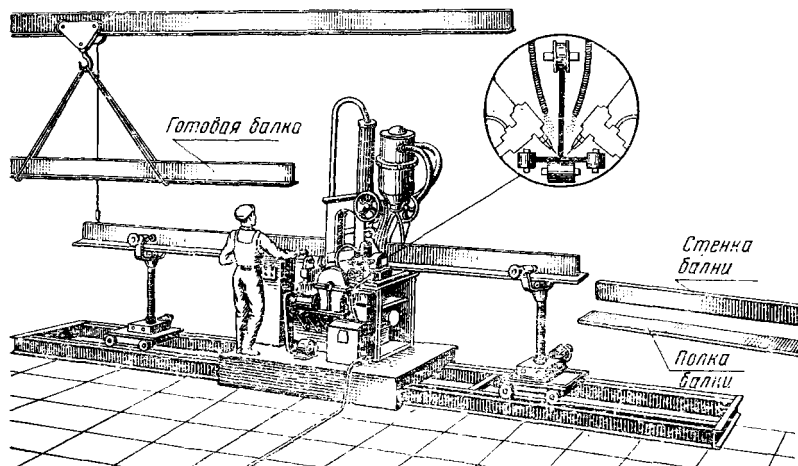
Сборка и сварка тавровых балок на станке «СТС» (в круге — схема сборки и сварки втавр)
